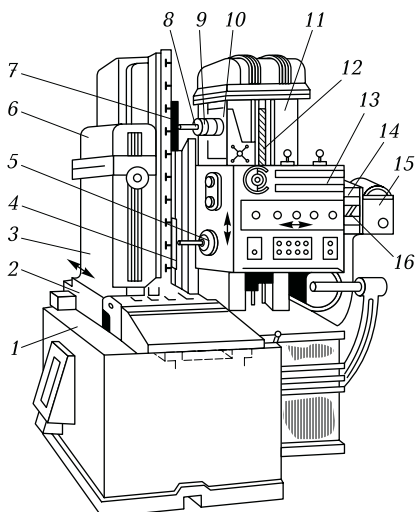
Копировально-фрезерный станок с горизонтальным расположением шпинделя и электрической следящей системой:
